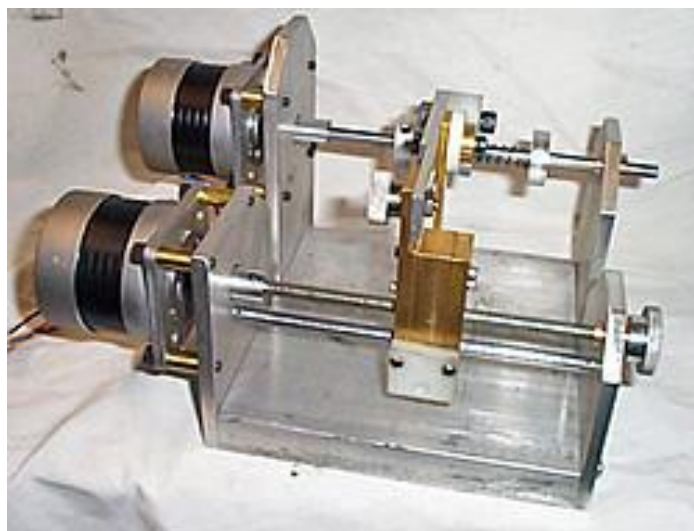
4 Coil Winding machine mk1.2 Převzato z [35]
